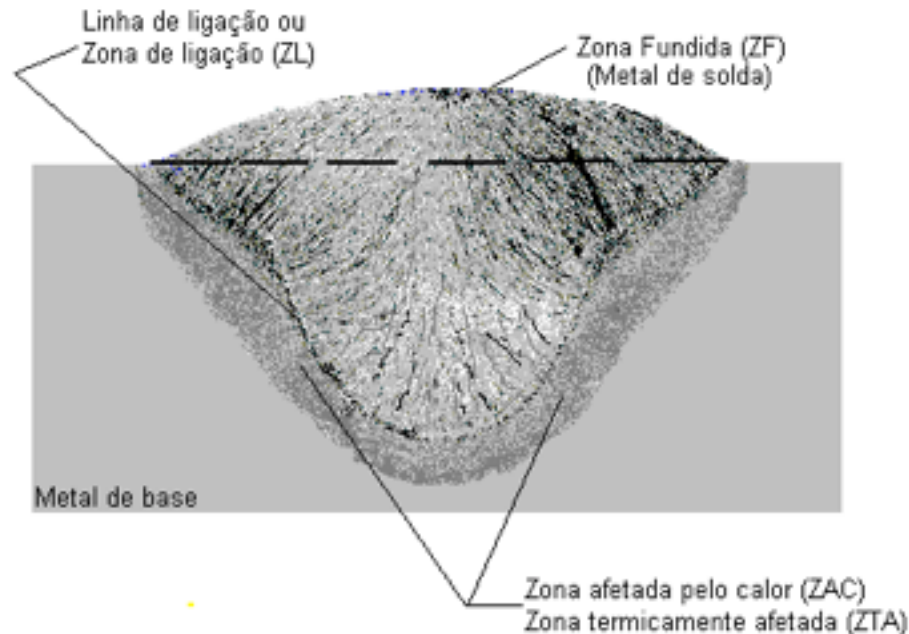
Vista transversal de um cordão de solda sobre chapa.
